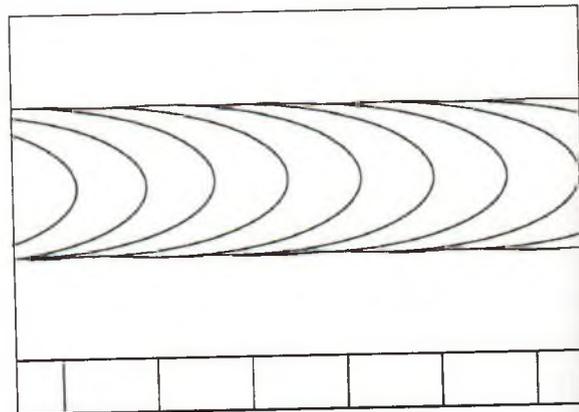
Стыковое сварное соединение обечайки сосуда. Автоматическая сварка в среде защитных газов.
